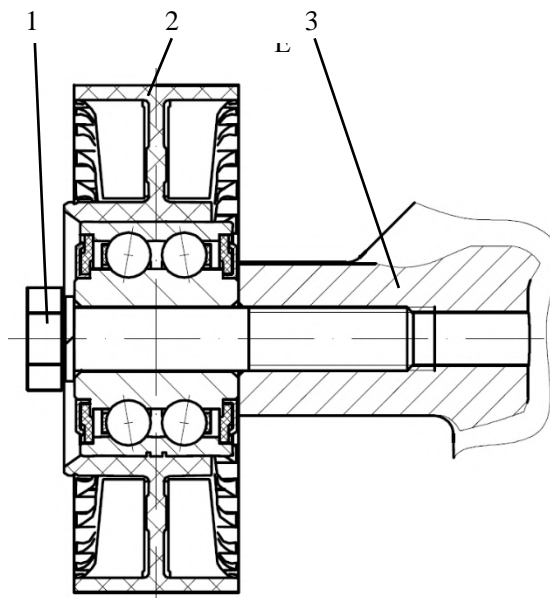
Ausrichtung der mit M10-Schrauben zu befestigenden Führungsrollen bei der Montage:
